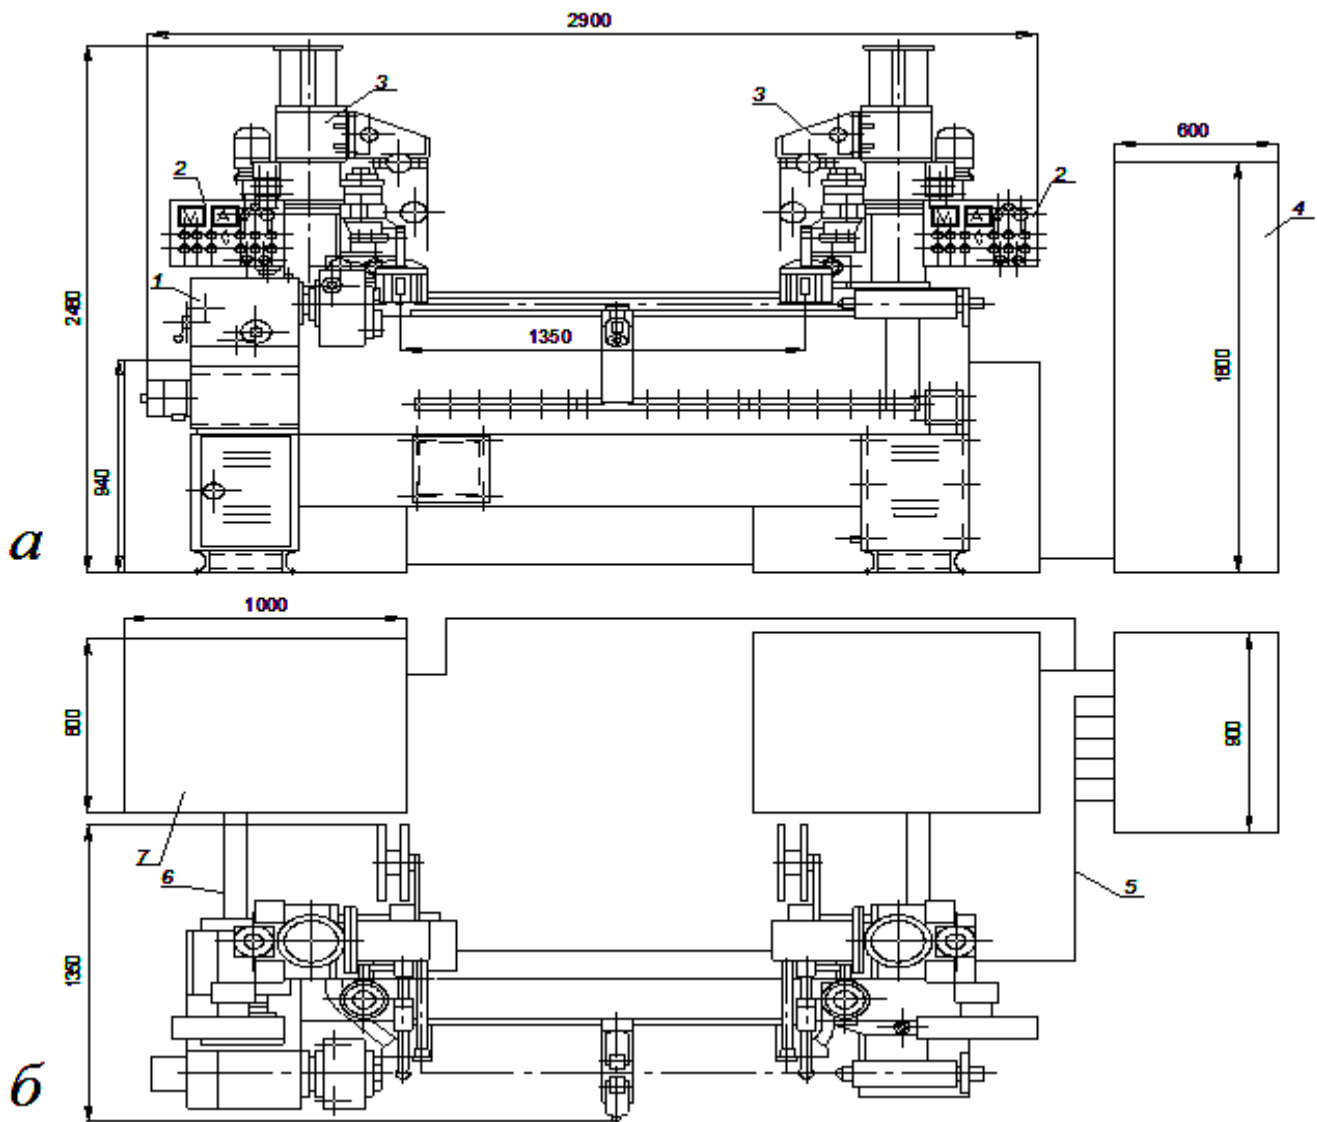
Універсальний верстат УД 123 для дугового зварювання у вуглекислому газі:
